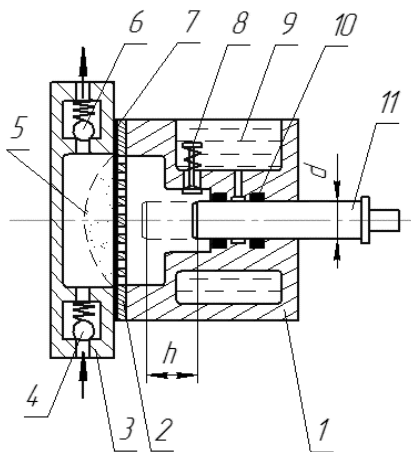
Мембранний насос: 1 – корпус; 2 – перфорована мембрана; 3 – розподільний диск; 4 – клапан всмоктування; 5 – камера робоча; 6 – клапан напірний; 7 – резино-тканинна мембрана; 8 – клапан компенсаційний; 9 – резервний бак; 10 – ущільнення плунжера; 11 – плунжер
